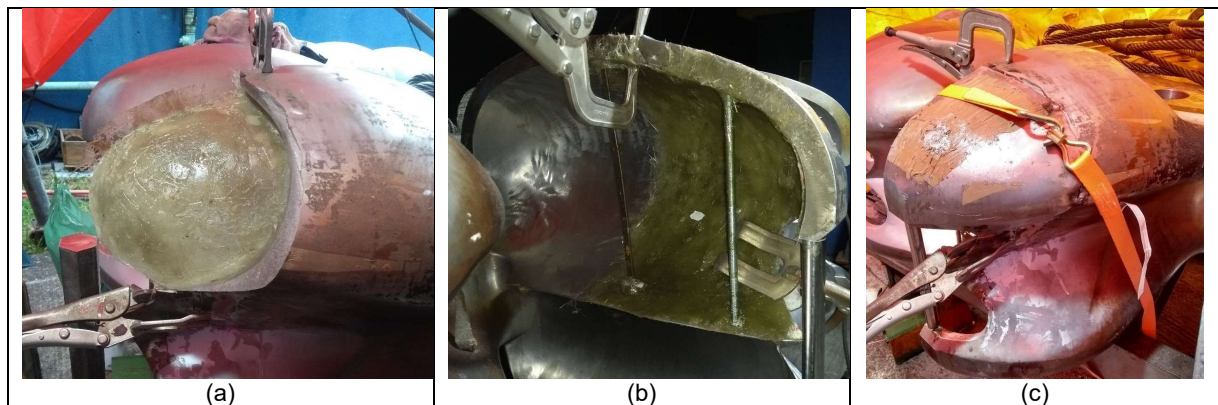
(a) após posicionamento do molde de fibra de vidro, (b) Posicionamento da seção fraturada sobre o molde e barra de apoio e (c) Posicionamento e ponteamto da seção fraturada ao restante da concha.
